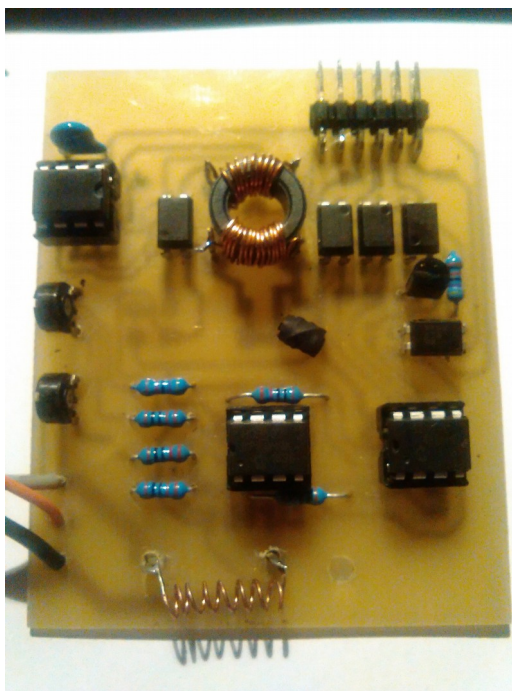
Motiv desky s plošnými spoji - Základní deska
